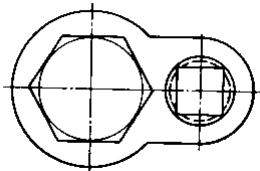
Головка S= 46 для регулировки зазоров в клапанах
